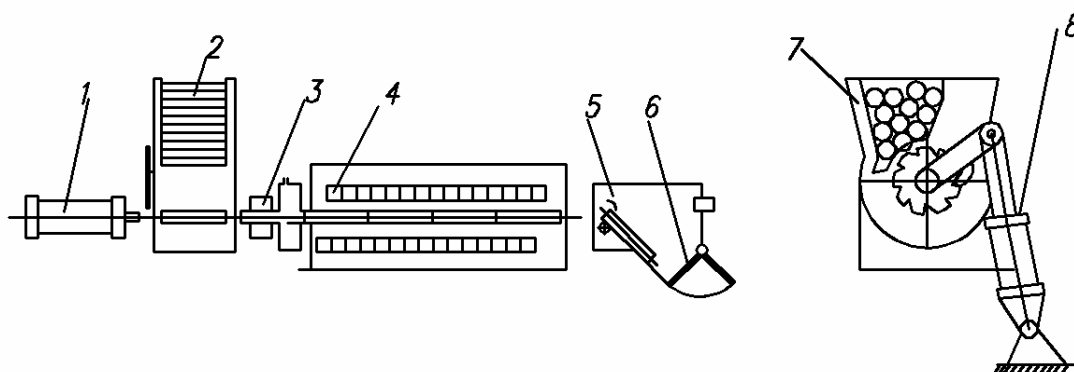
Нагреватель для безокислительного нагрева заготовок в защитной атмосфере: 1 – толкатель; 2 – магазин; 3 – уплотнительная камера; 4 – индуктор; 5 – камера выдачи заготовок; 6 – заслонка; 7 – барабан; 8 – цилиндр поворота барабана
